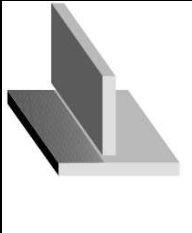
Posiciones de Soldadura <sup>2</sup>
